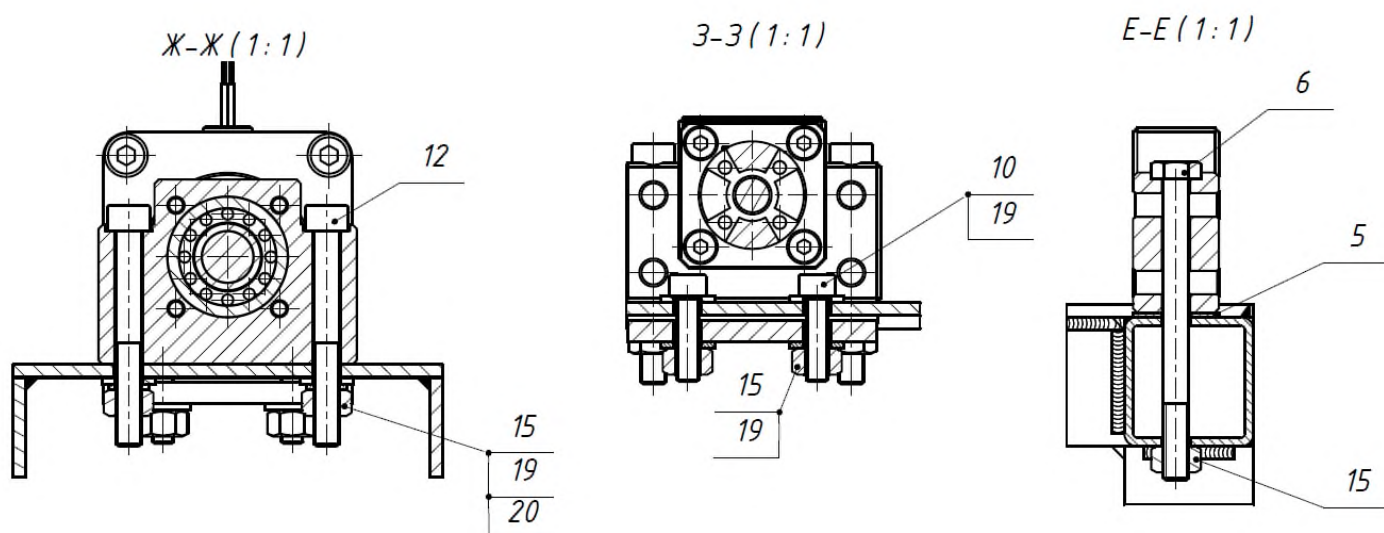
Загальний вигляд верстату для гібридної обробки струминно-лазерним методом (закінчення).
